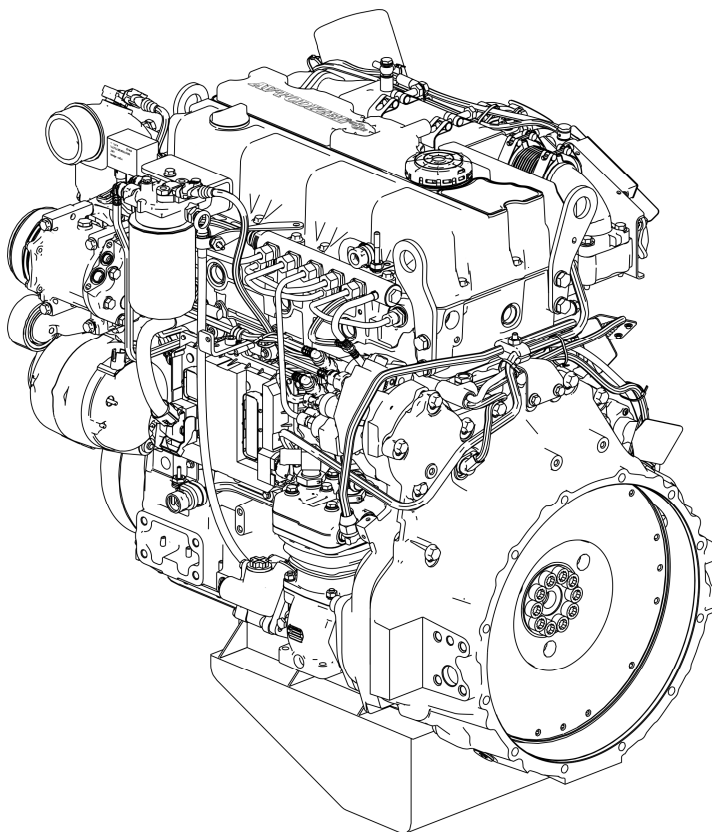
Двигатель ЯМЗ-53472-10 – общий вид слева
